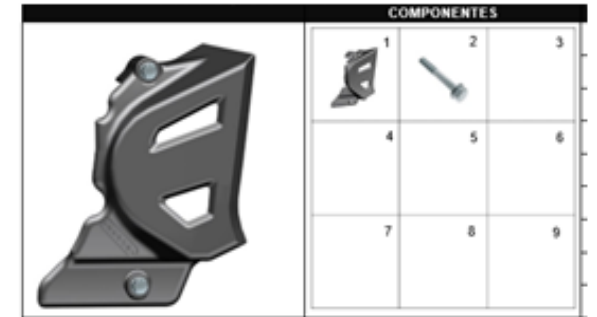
TAPA TRA SERA IZQUIERDA MOTOR
